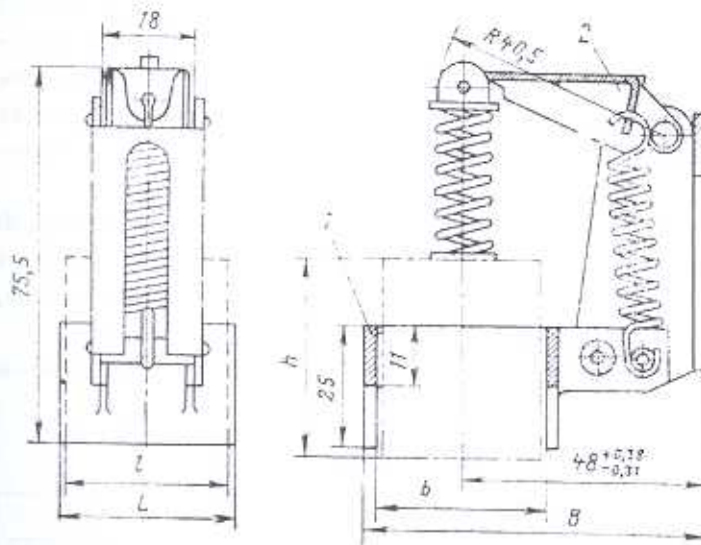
Щеткодержатель радиальный типа ДГ; основные размеры:
